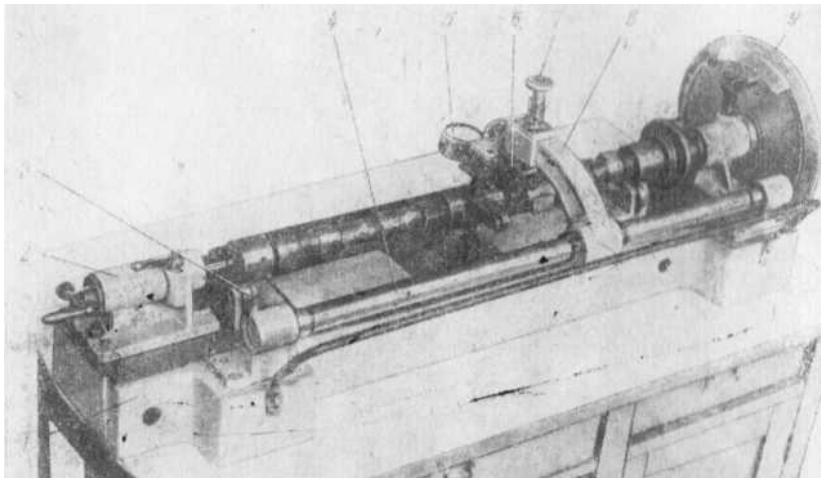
Приспособление для контроля кулачков распределительного вала
